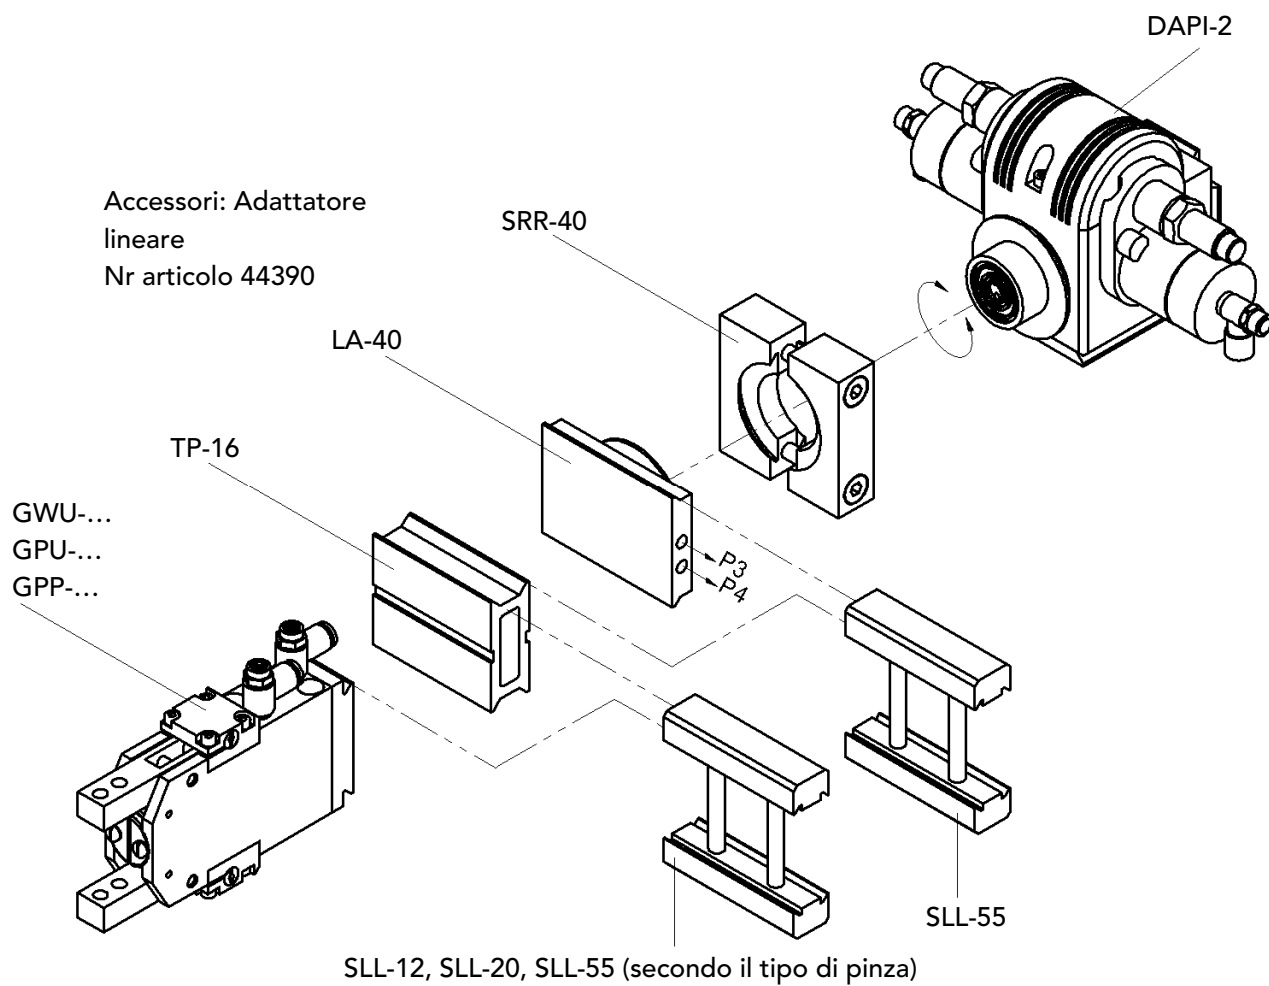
L'asse della pinza è ad angolo retto rispetto all'asse di rotazione
